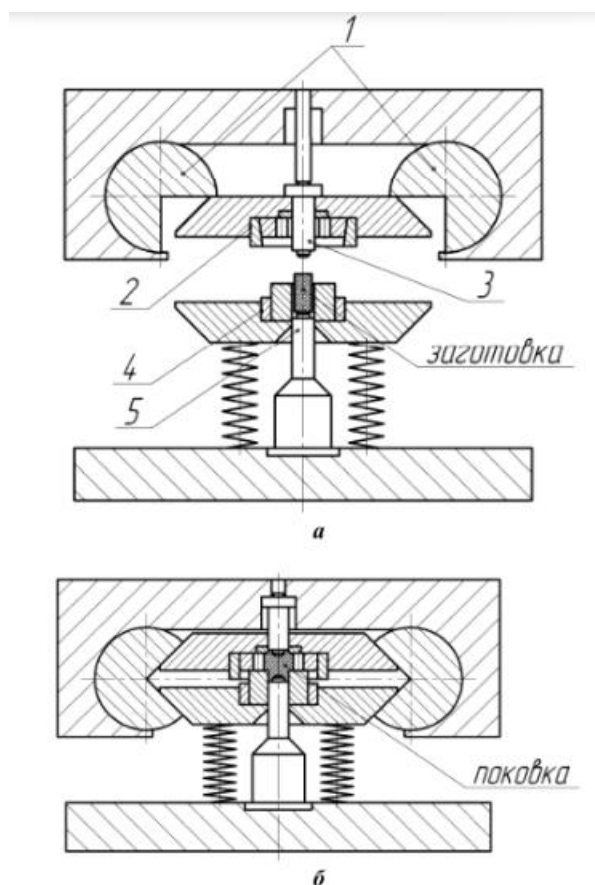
Штамп для комбинированного выдавливания с разъемными матрицами: а) заготовка установлена в штамп; б) рабочее состояние
